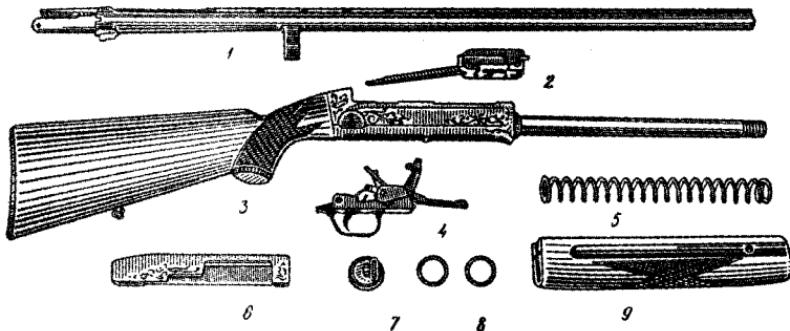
Ружье МЦ21-12 при неполной разборке: 1 - ствол, 2 - затвор в сборе, 3 - коробка и ложа в сборе, 4 - ударно-спусковой механизм, 5 - возвратная пружина ствола, 6 - крышка коробки, 7 - колпачок цевья, 8 - тормоз ствола, 9 - цевье в сборе.
